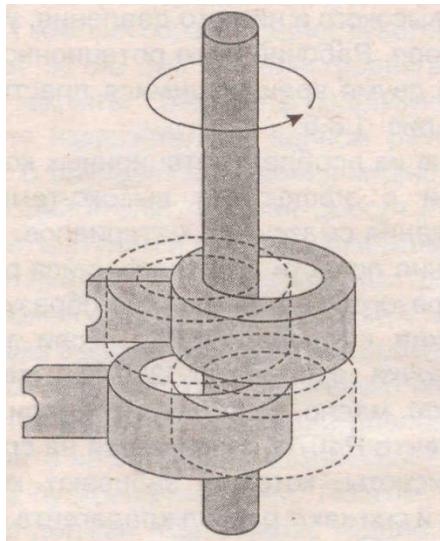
Противофазное расположение роторов на валу двухроторного компрессора.
